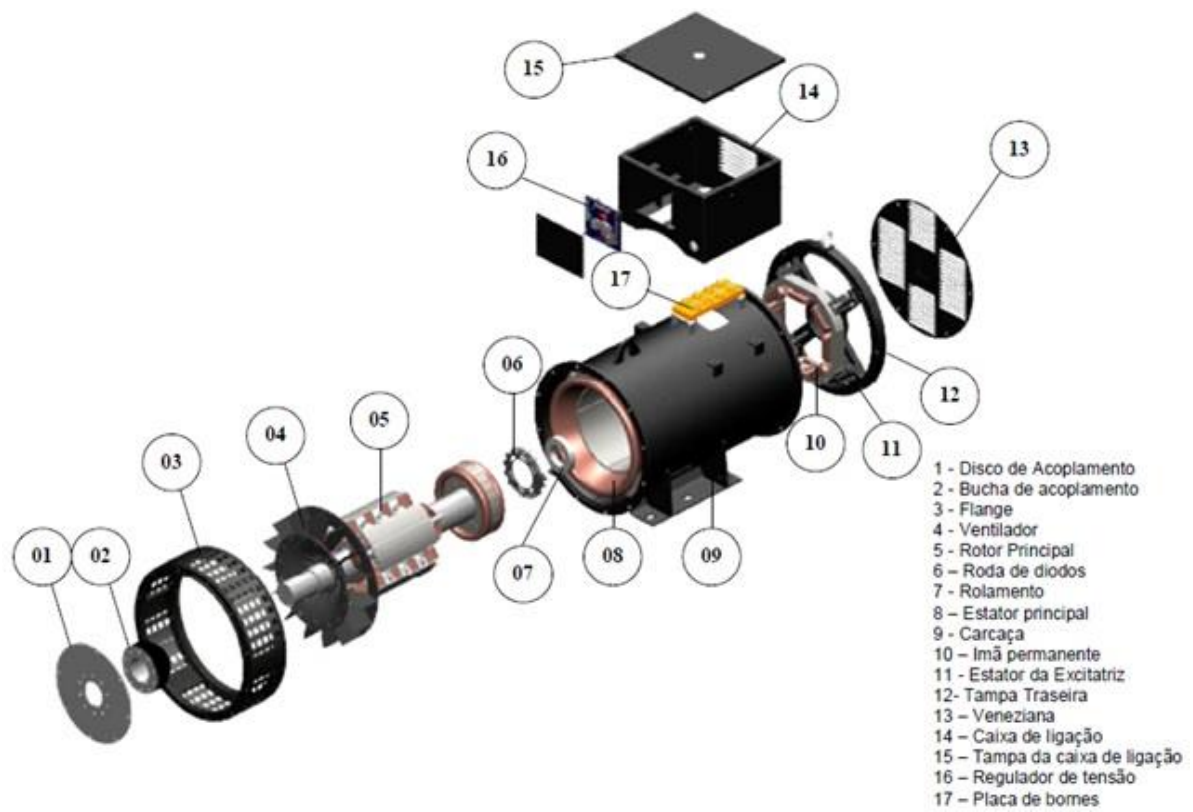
Desenho explodido de gerador GPA 312 EE DI
